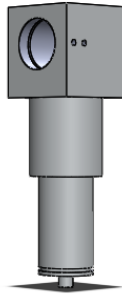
Primer eslabón del sistema (ensamblaje de piezas A y B).
